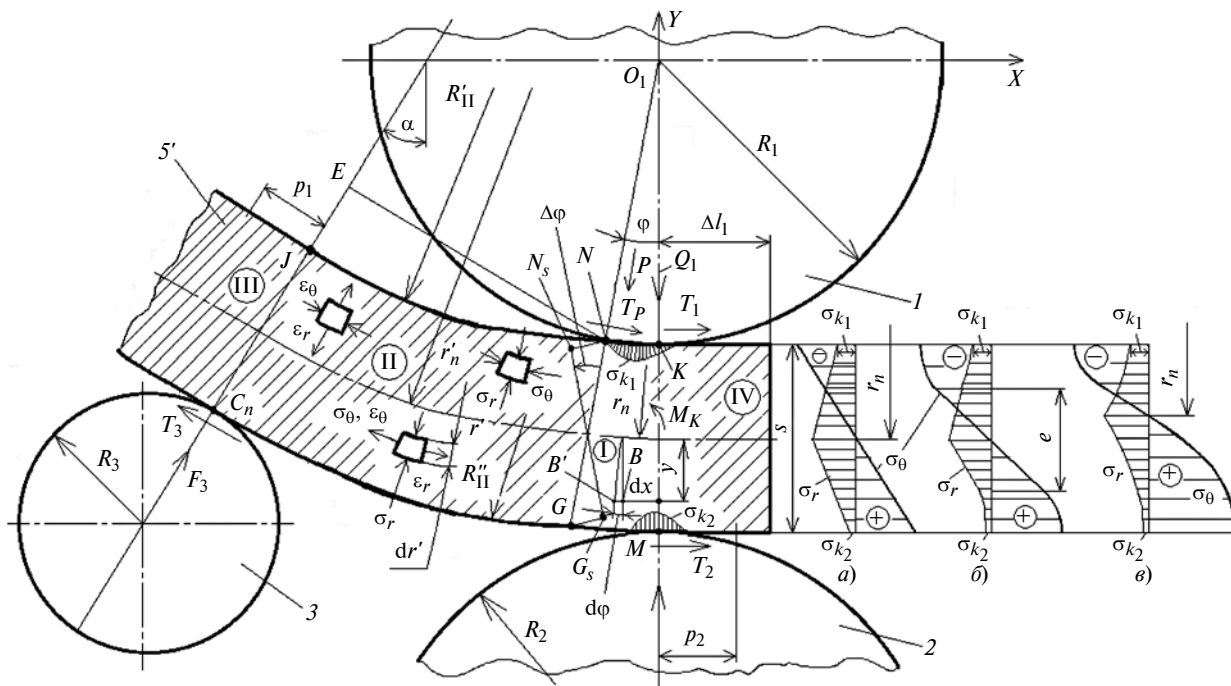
Схема для расчета напряжений по толщине в конце подгибки заготовки
